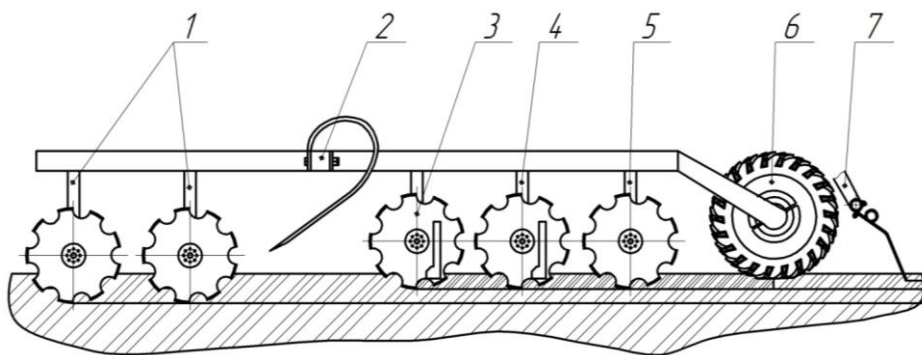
Дисковый культиватор Carrier фирмы Väderstad
